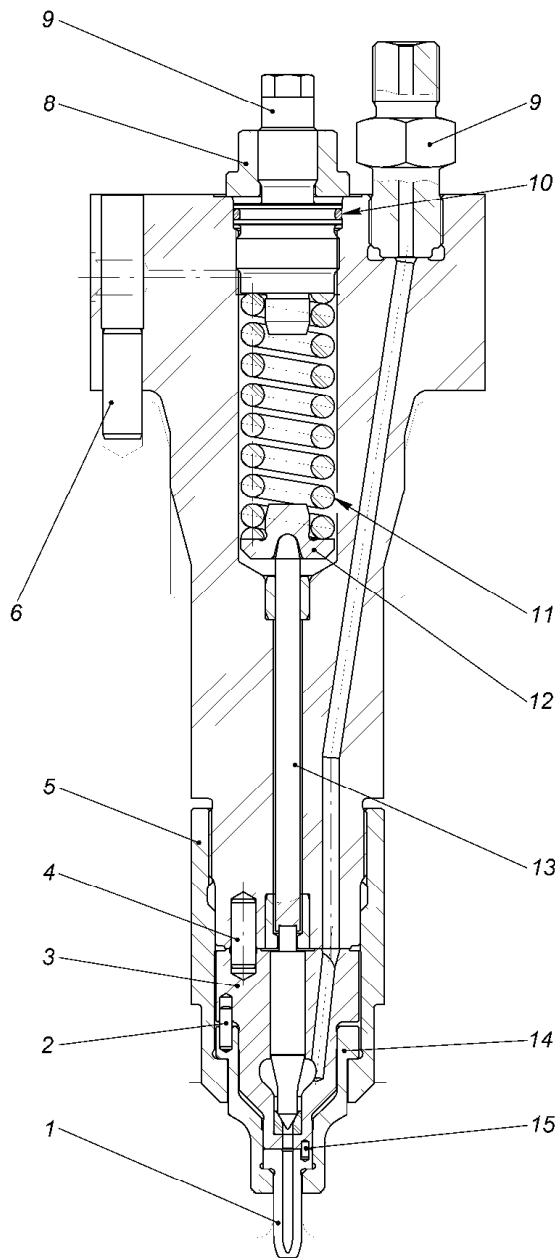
Форсунка двигуна RTA 72: 1 – корпус розпилювача; 2 – установочний штифт; 3 – корпус голчастого клапана; 4 – установочний штифт; 5 – накладна гайка; 6 – установочний штифт; 7 – контргайка; 8 – регулювальний гвинт; 9 – штуцер підведення палива; 10 – ущільнення регулювального гвинта; 11 – пружина; 12 – упорна тарілка; 13 – шток; 14 – прокладка; 15 – установочний штифт
